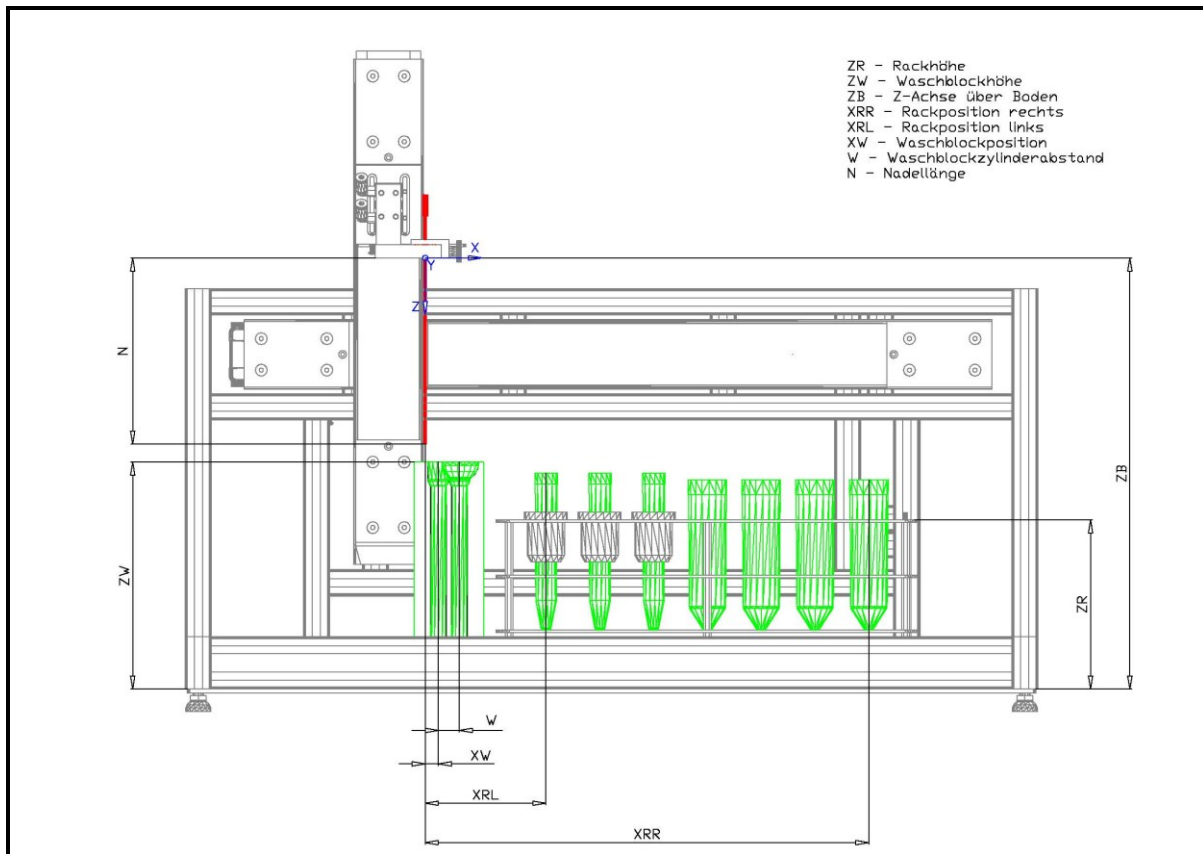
Technische Zeichnung der Frontansicht des SV-LH
